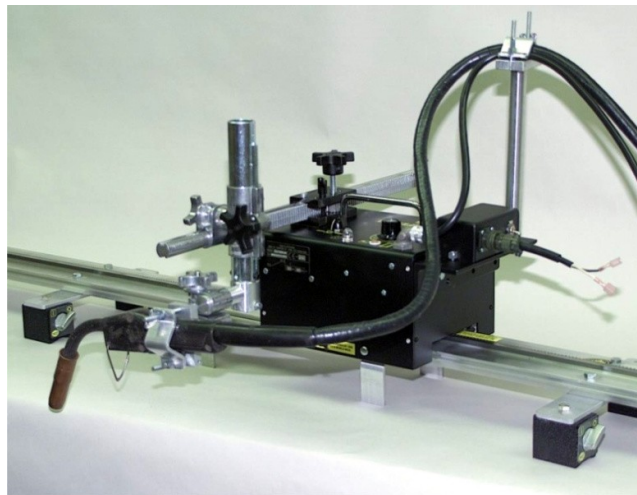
GO-FER III: Manipulador para soldagem da empresa BUG-O com um grau de liberdade (32)
